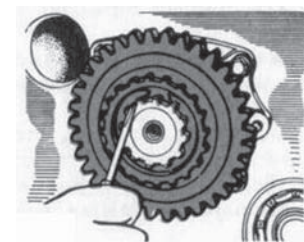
Снятие стопорного кольца и ведомой шестерни понижающего редуктора.
